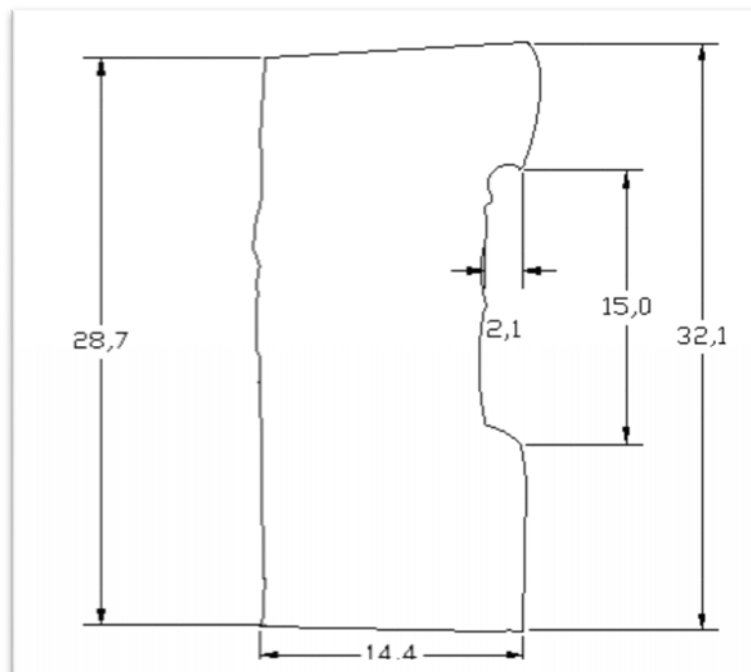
Pieza soldada a rotor (Fotogrametría)
